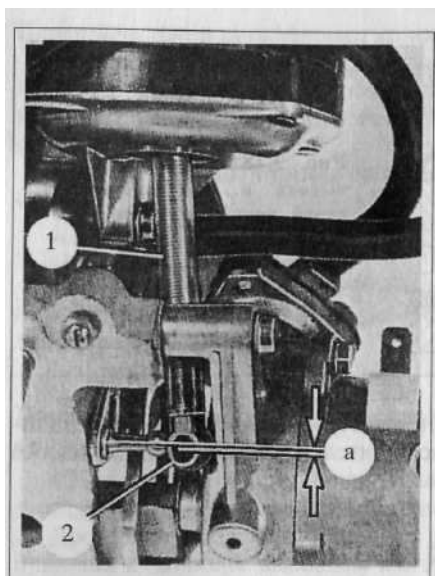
Регулировка тяги привода 2-й камеры:
